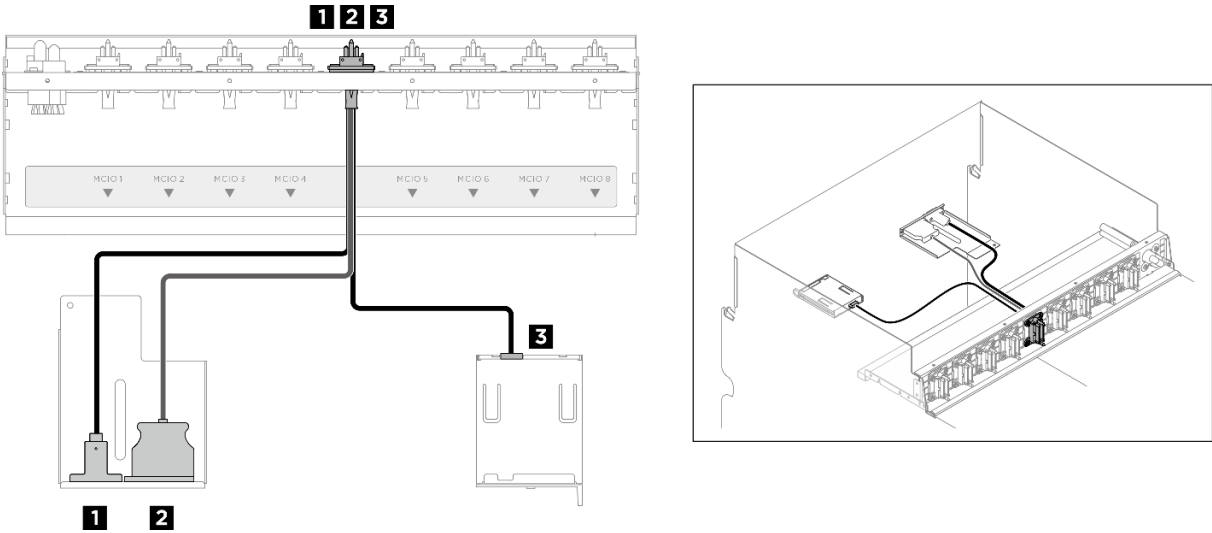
Instradamento dei cavi del modulo I/O anteriore e del pannello di diagnostica integrato
